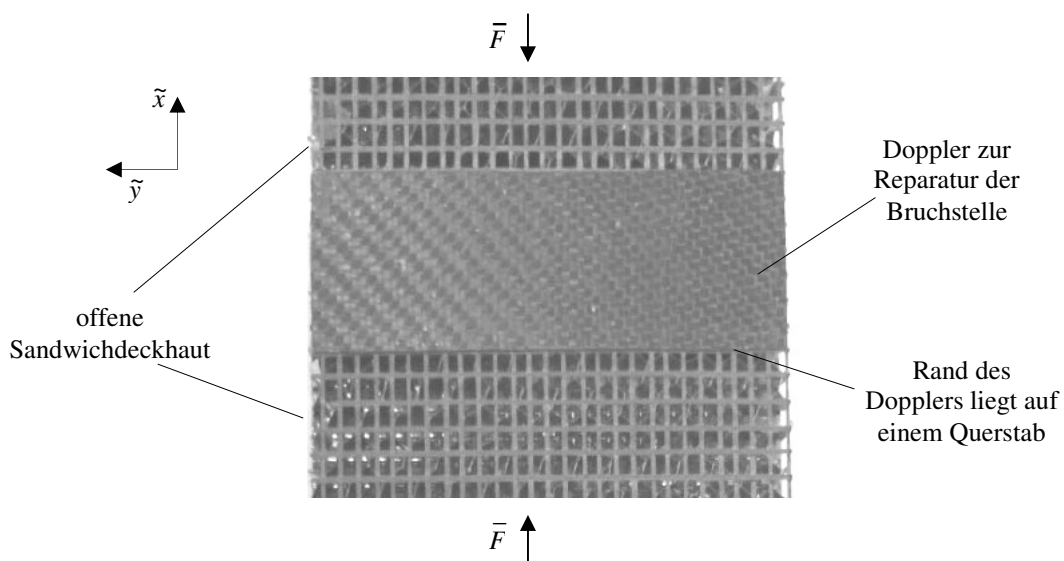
Geprüfter Probekörper mit reparierter Bruchstelle
